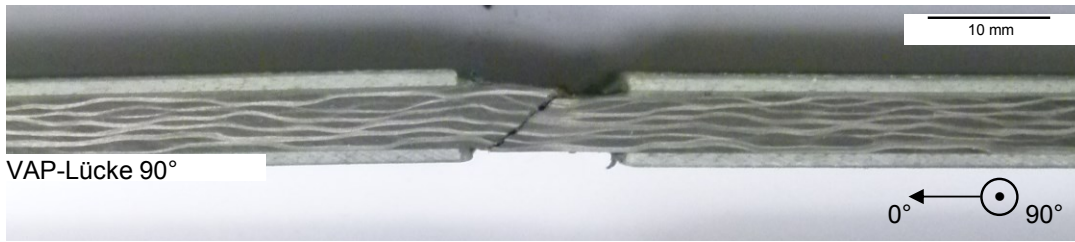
Bruchbild einer VAP-Lücke 90°-Druckprobe
